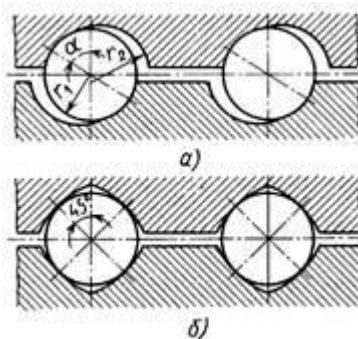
Профиль канавок передачи винт-гайка качения
